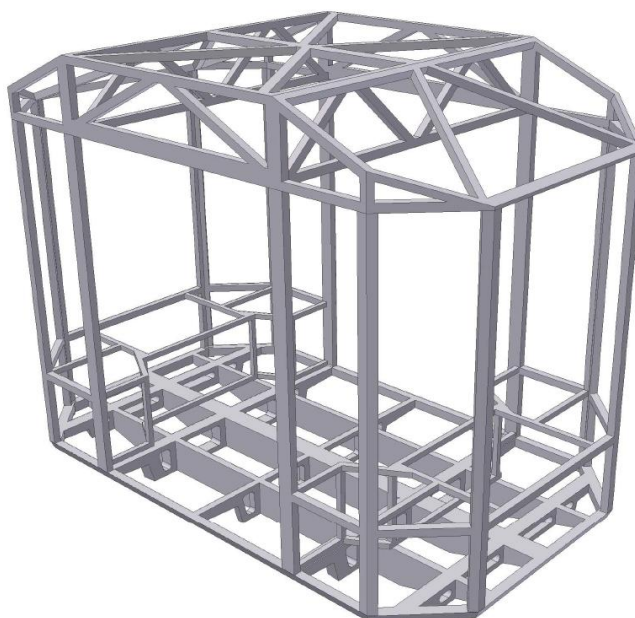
Каркас сварной юнибуса Ю-324П исполнения 02
